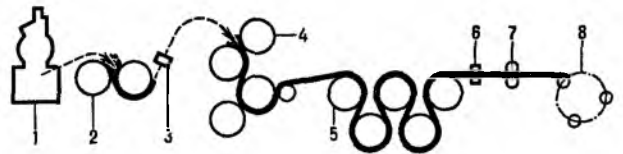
Производство изделий каландрованием: 1 — смеситель; 2 — валцы; 3 — детектор металла; 4 — S-образный наклонный каландр; 5 — охлаждающие барабаны; 6 — толщиномер; 7 — устройство для обрезания кромок; 8 — закаточное устройство.
